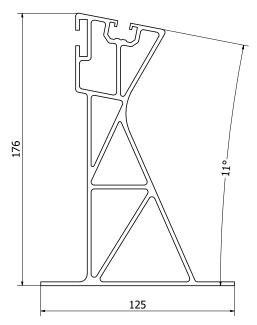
Hoher Aluminium-Montagewinkel K-45-7
